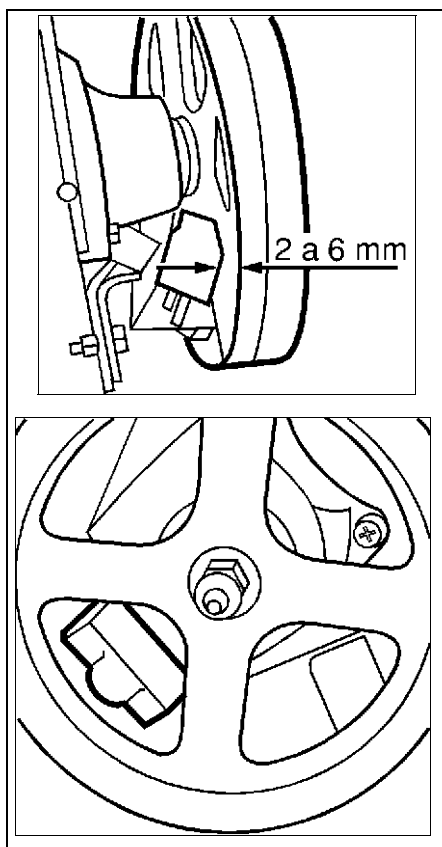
Posición del sensor de rotura de la correa del ventilador.
